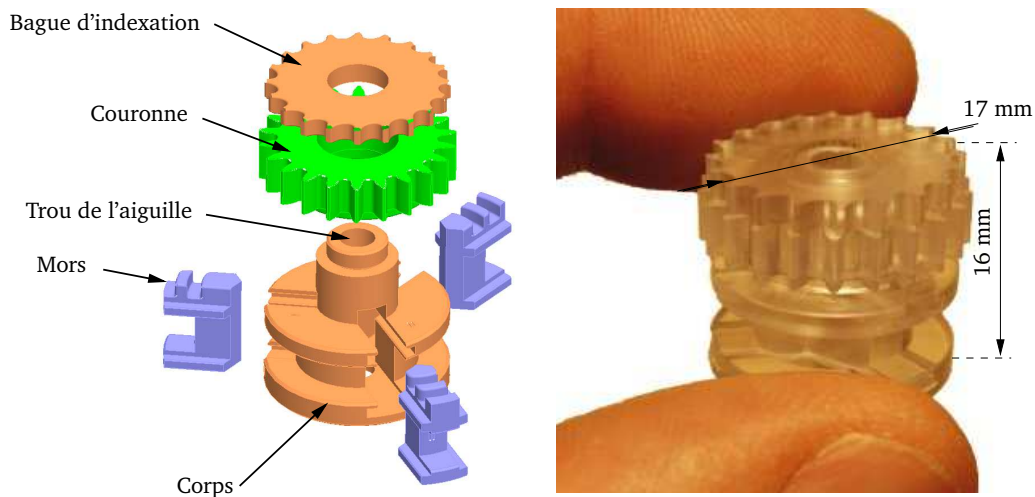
Vue CAO éclatée et prototype de mandrin à trois mors.
